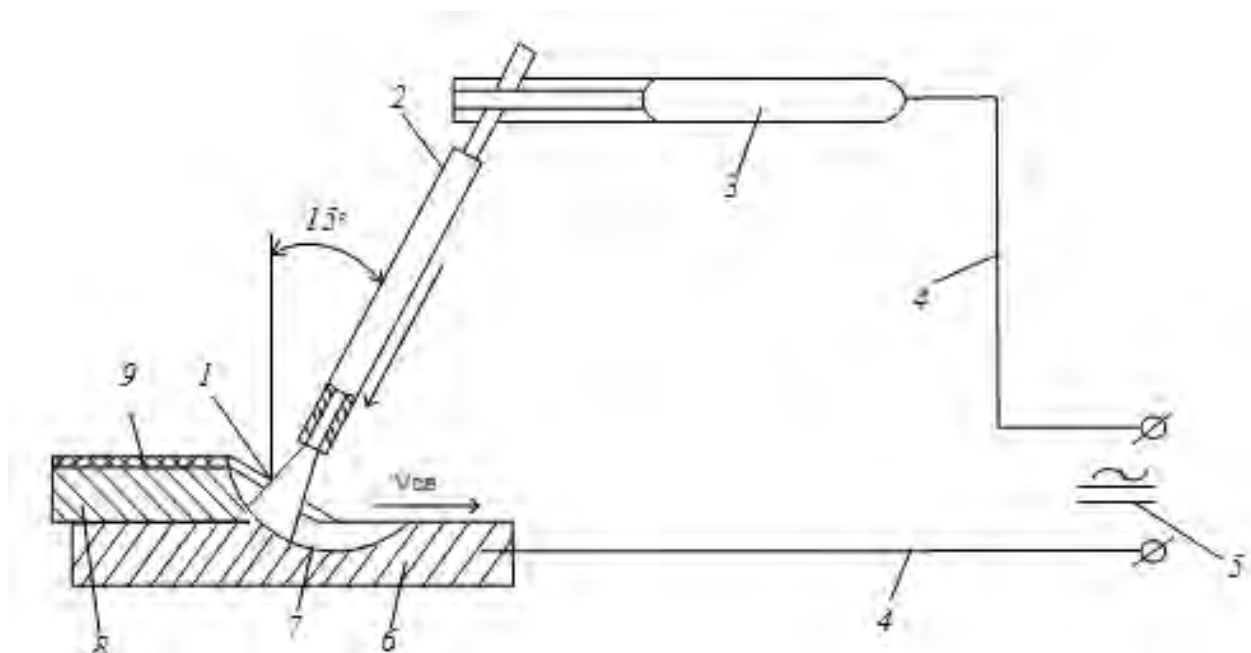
Схема ручной сварки покрытым электродом:
